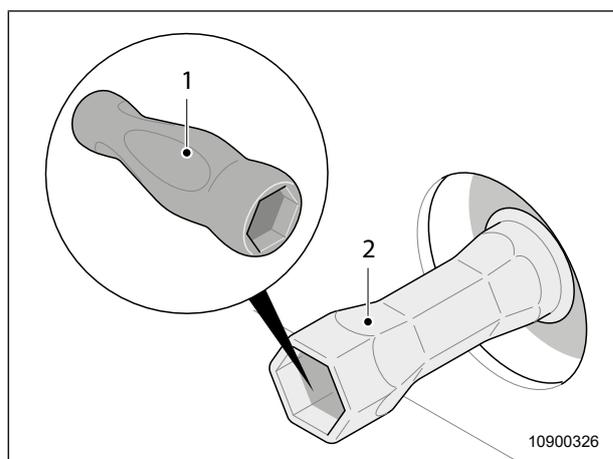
Mutter Heckleuchte mit Griff aus dem Bordwerkzeug
